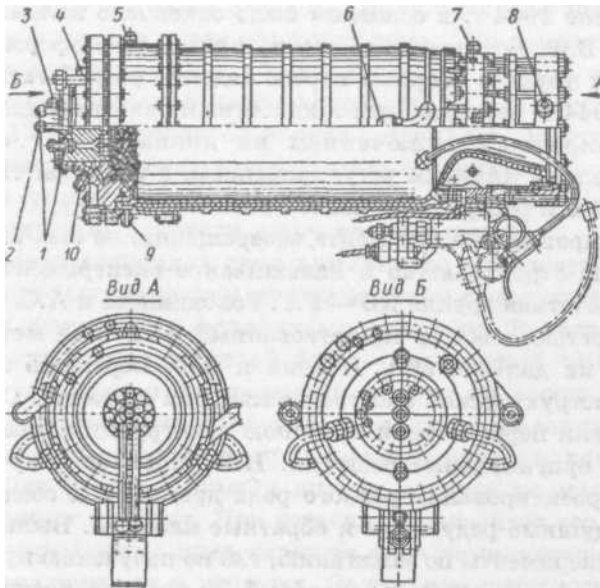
Жидкостный ракетный двигатель РД-1 разработки А.М. Исаева [18]:
